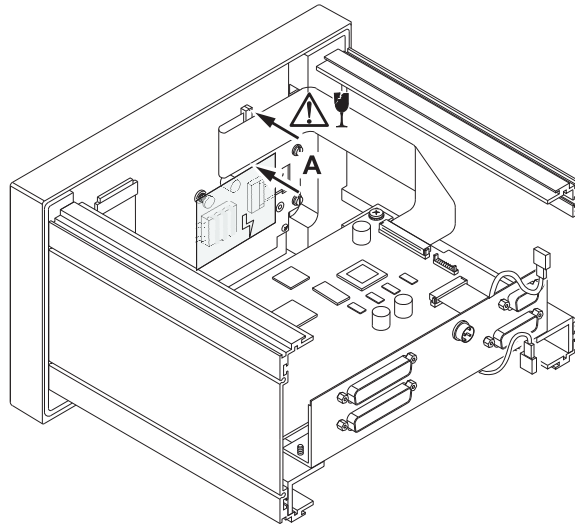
Aufstecken des Flachband-Anschlusskabels auf die Displayplatine
